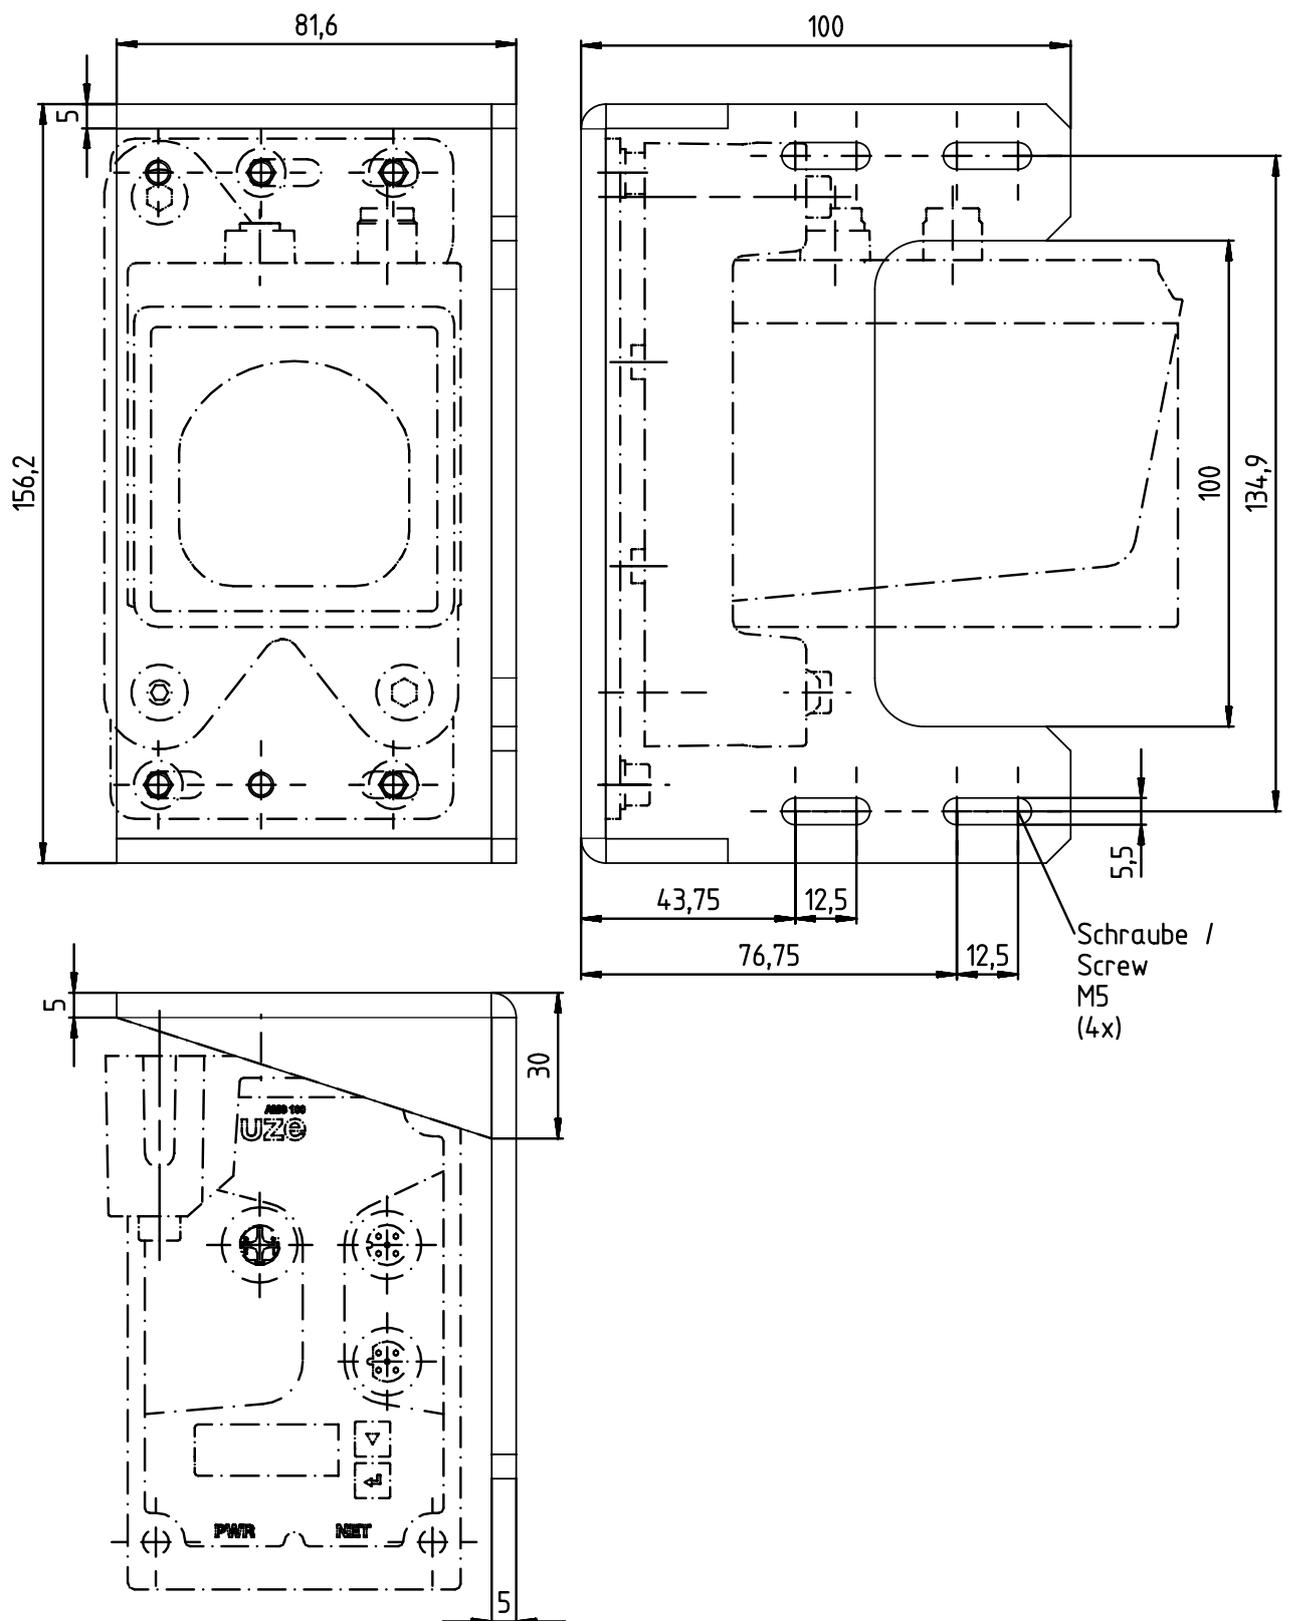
Encombrement de la pièce MW OMS/AMS 01
